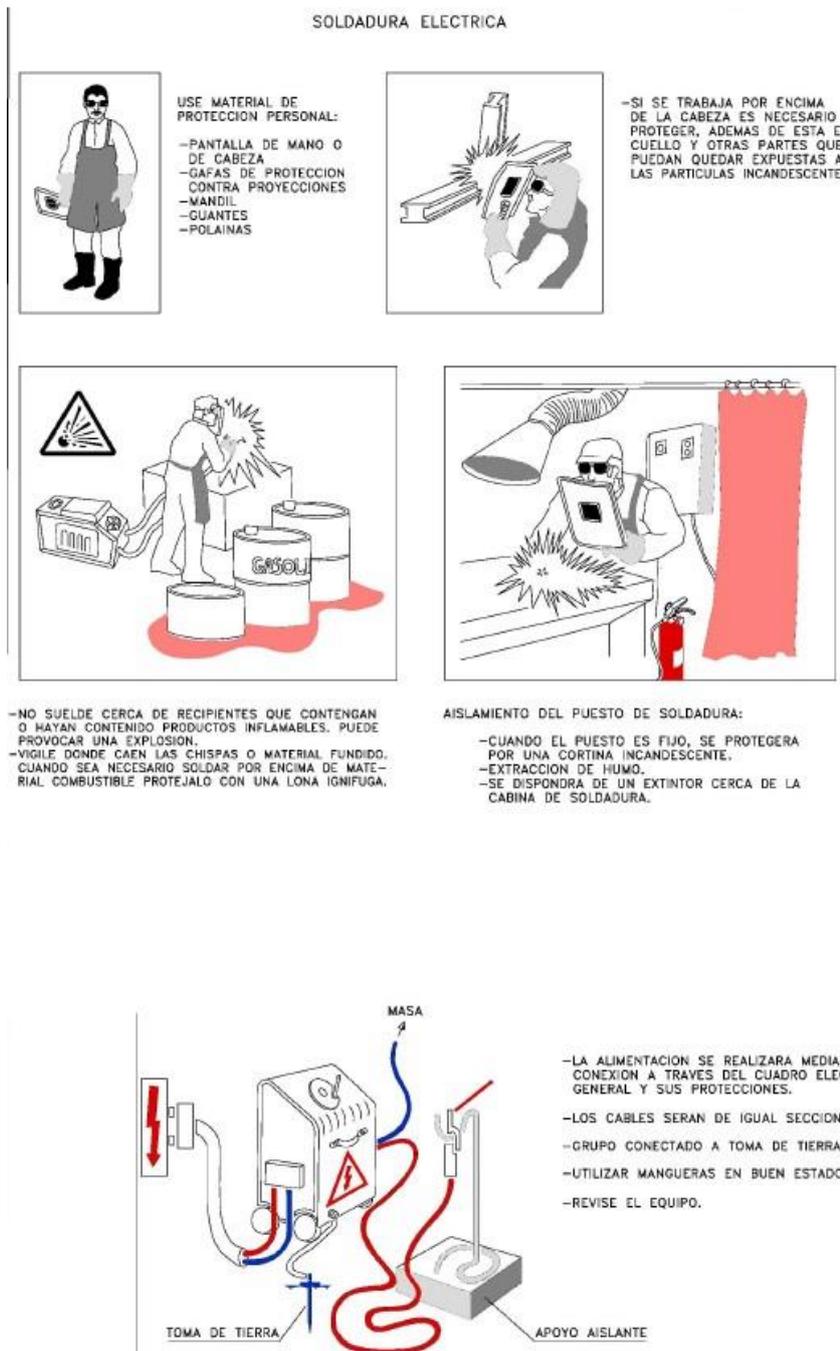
TRABAJOS DE SOLDADURA ELÉCTRICA
